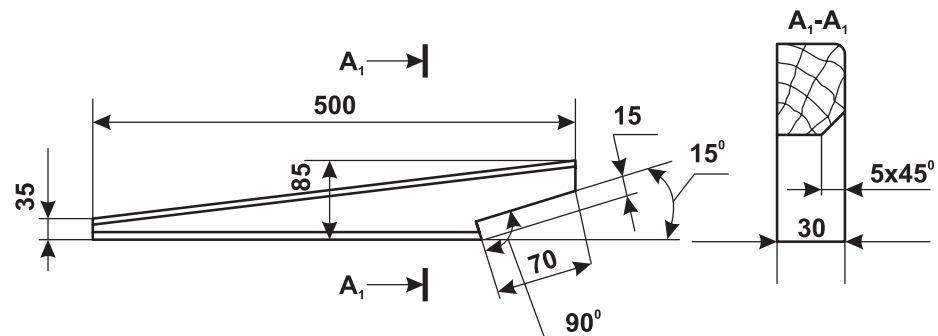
Толкатель для деревянной заготовки при пилении
